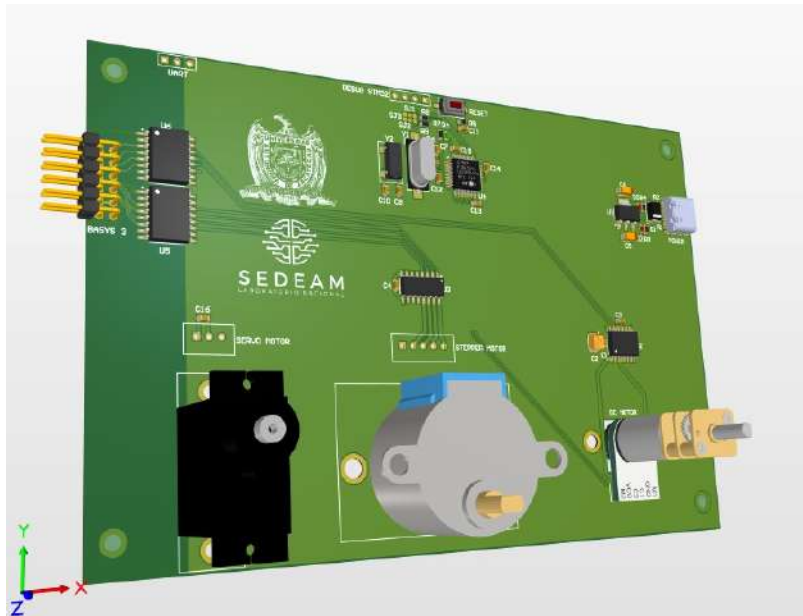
Vista 3D del diseño físico de la PCB con motores integrados
